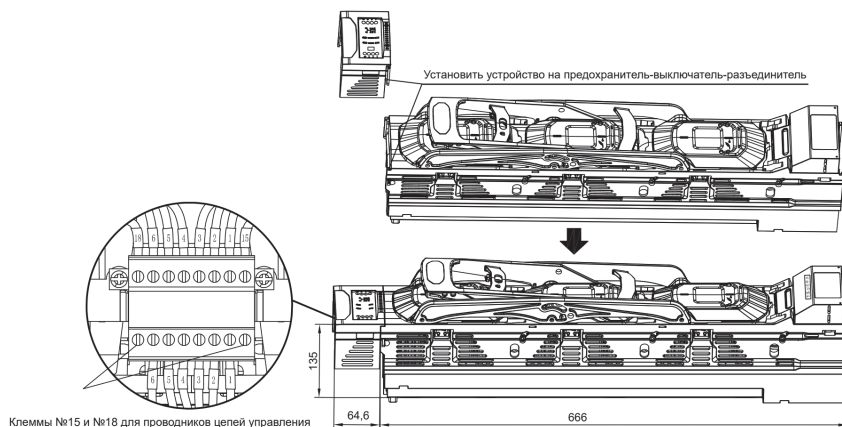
Установка устройства на предохранитель-выключатель-разъединитель
